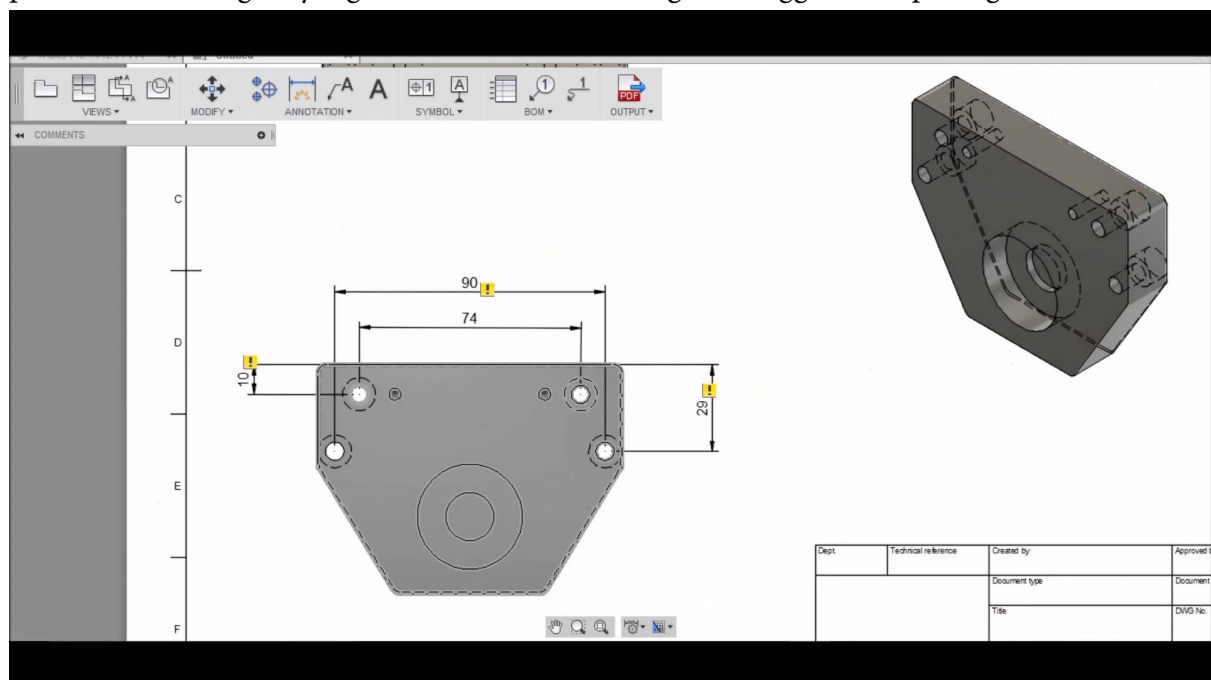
konversi drawing 2 dimensi ke solid obyek 3 dimensi
